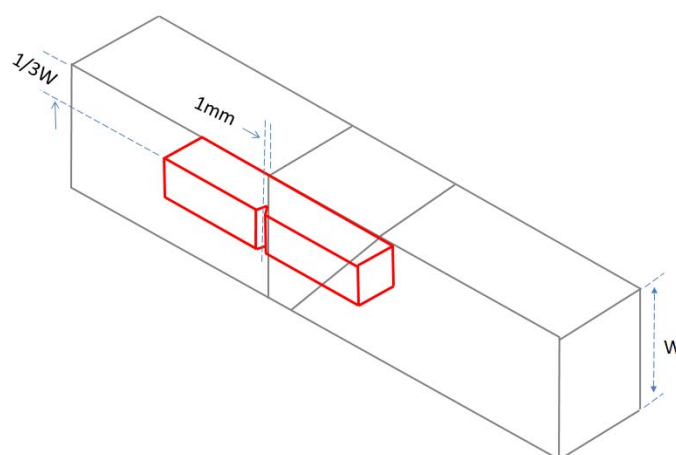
Retirada de corpo de prova charpy da junta soldada.
